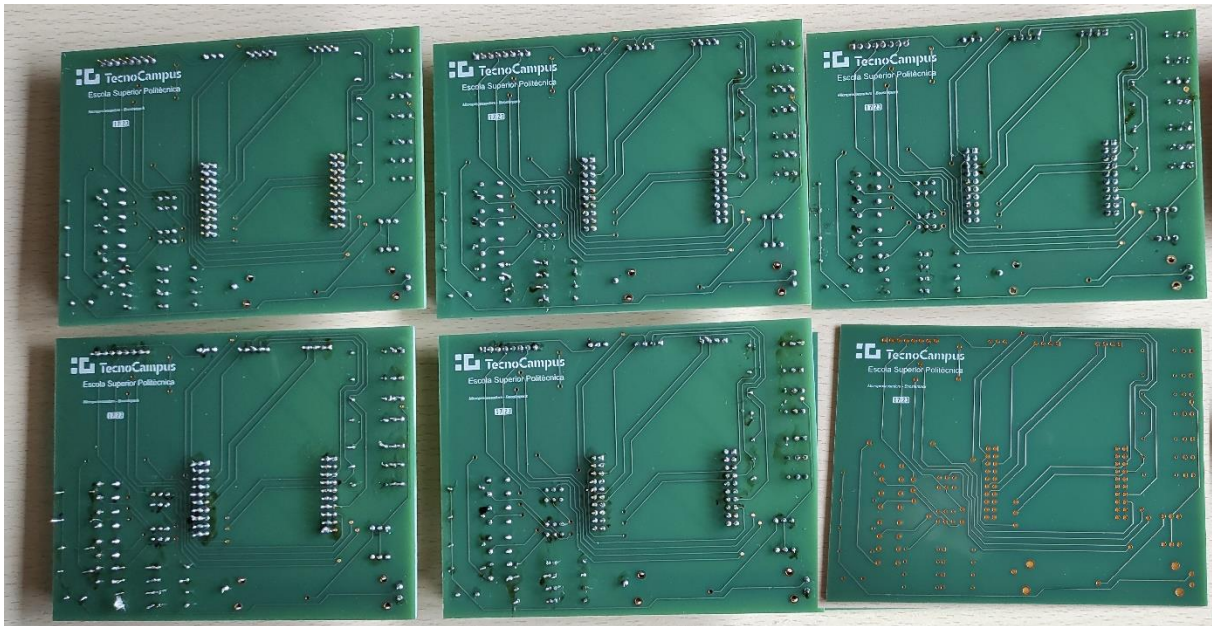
Vista de darrere de les 5 PCBAs i la PCB sobrant.
